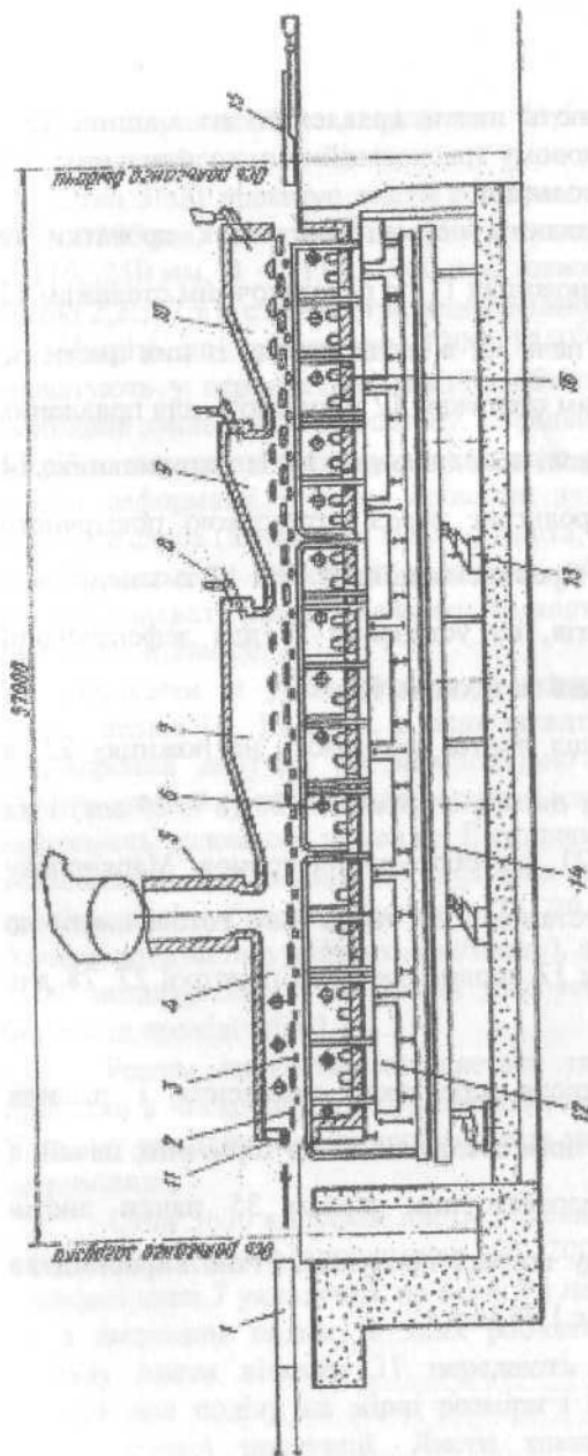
Схема нагрівальної пічі з крокуючими балками :
